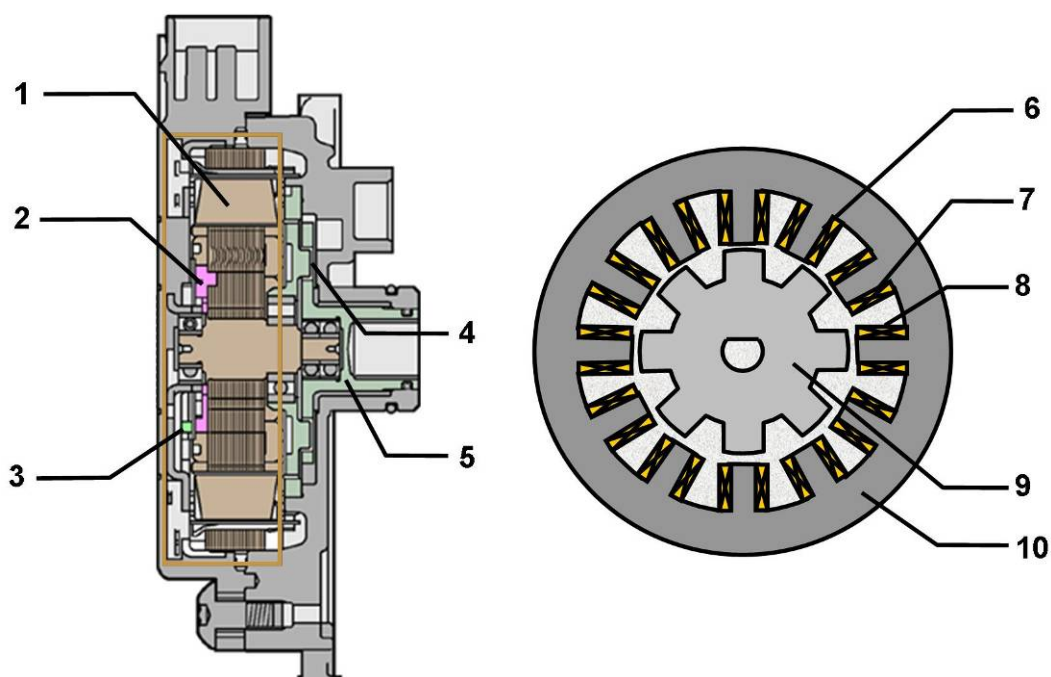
Исполнительный механизм блокировки рычага селектора в положении «Р»:
